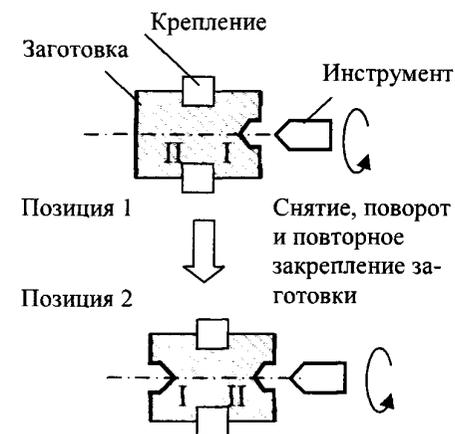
Схема центрования валика в один переход в два установка и в двух позициях
